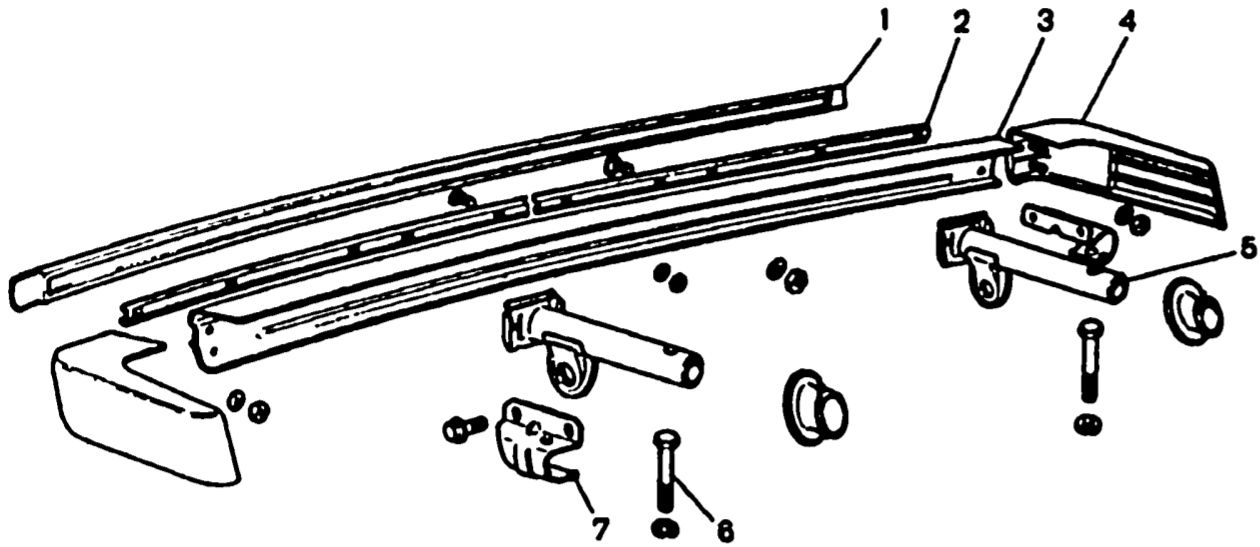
Задний бампер: 1 - накладка; 2 - держатель накладки; 3 - бампер; 4 - боковая накладка; 5 - трубчатый удлинитель; 6 - болт крепления; 7 - кронштейн
